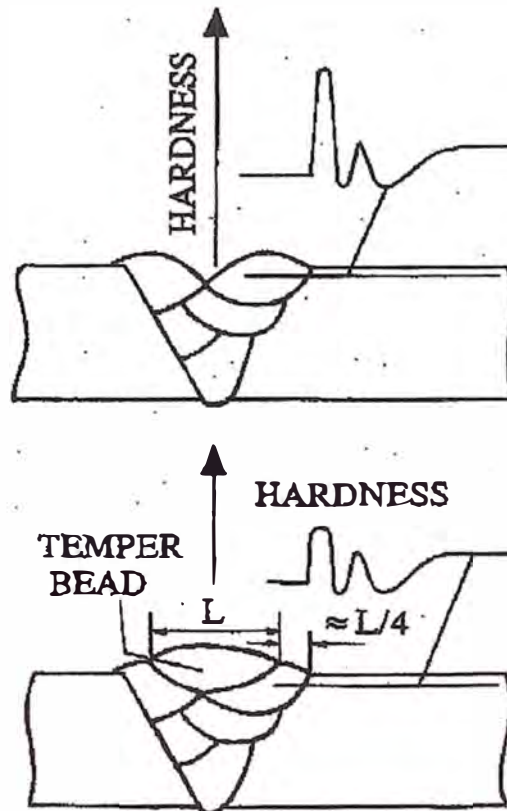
Reducción de un pico de dureza en la ZAC aplicando temper bead weld
